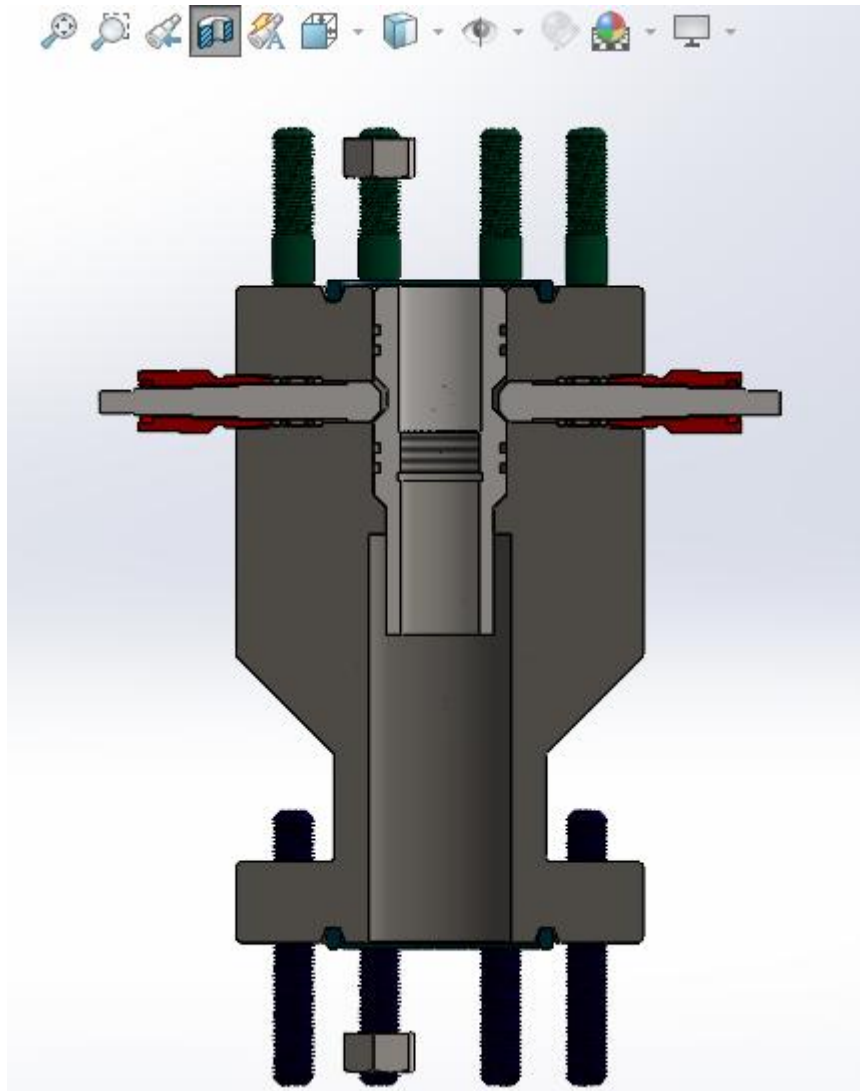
Vue en coupe de la Tubing Head assemblée sur SolidWorks
